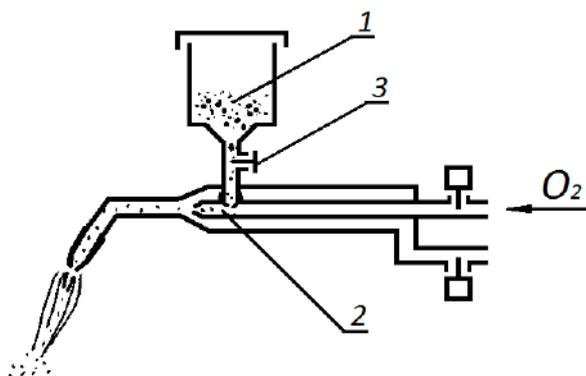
Схема горелки для газопорошкового напыления:
